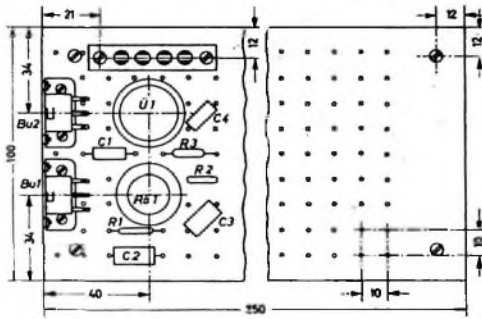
(links), Einzelteilanordnung und Abmessungen. Bild 3 (oben), Chassis-Gesamtdraufsicht. Bild 4, Chassis-Teilsansicht
